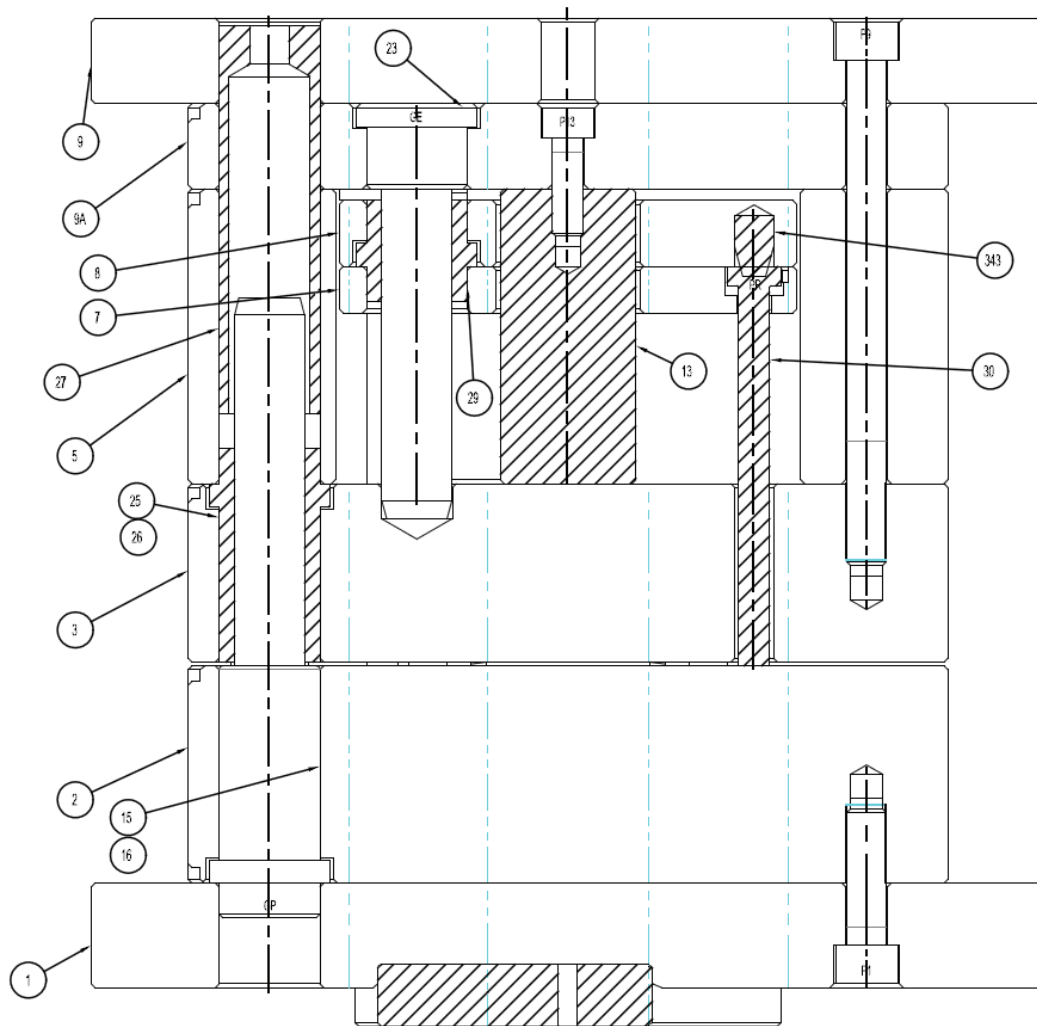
Molde de injeção com indicação dos vários componentes do molde 827 (vista em corte: seção B-B (desenho 2D final para montagem)).
